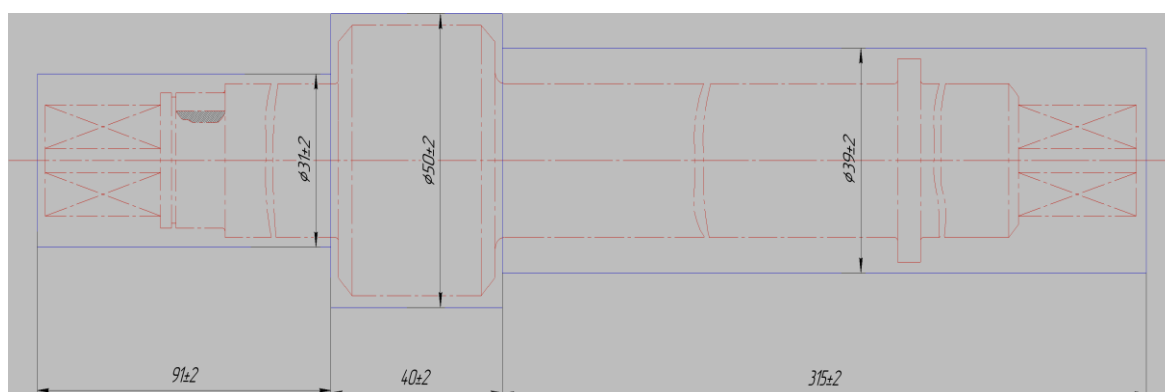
Эскиз заготовки из базового технологического процесса
